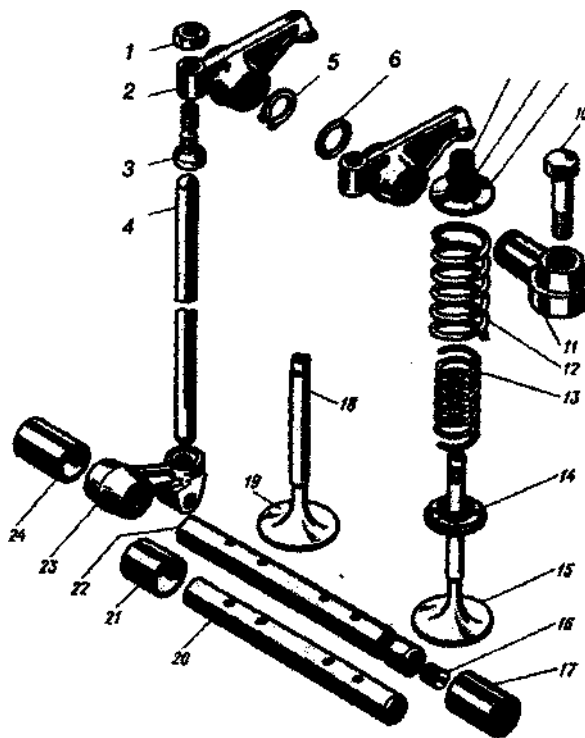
Деталі приводу клапанів двигунів ЯМЗ:
